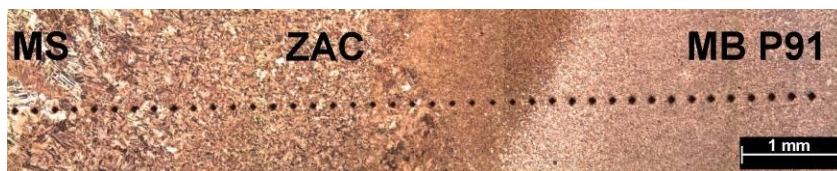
Macrografia da solda dissimilar correspondente ao DP25 no estado como-soldado, mostrando o MS, ZAC e MB P91. Ataque químico: Villela.
